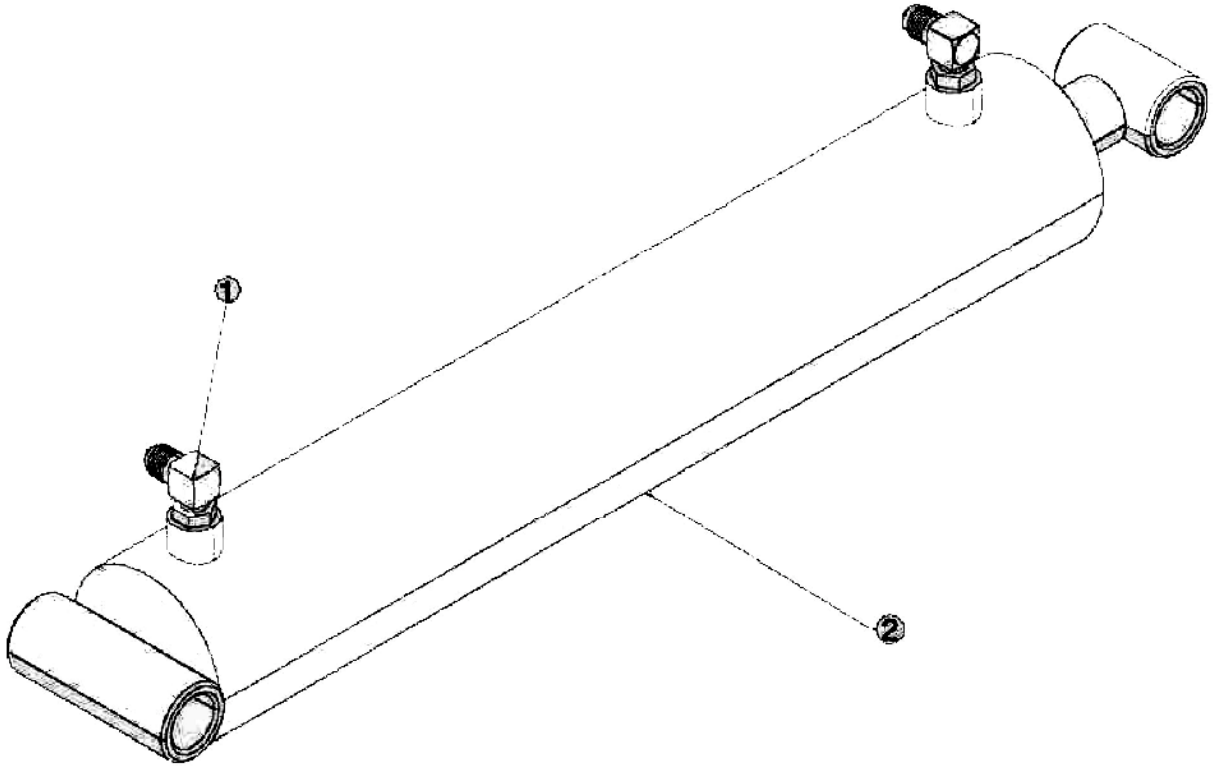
Чертеж гидравлического цилиндра механизма опрокидывания тележки-А801200
